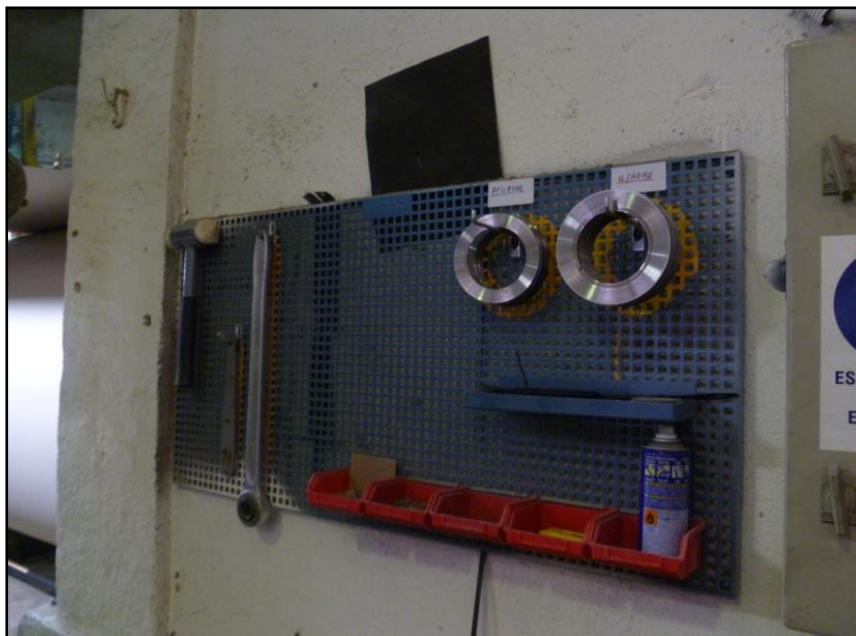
Panel de herramientas de la parte de detrás de la bobinadora
